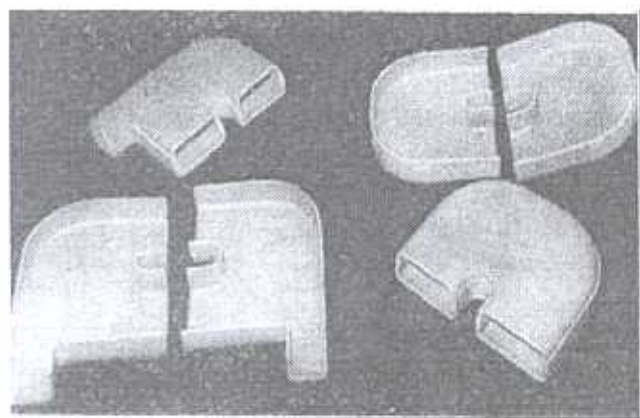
Детали пластмассовых коробок для изолировки головок стержней обмотки статора [2]
